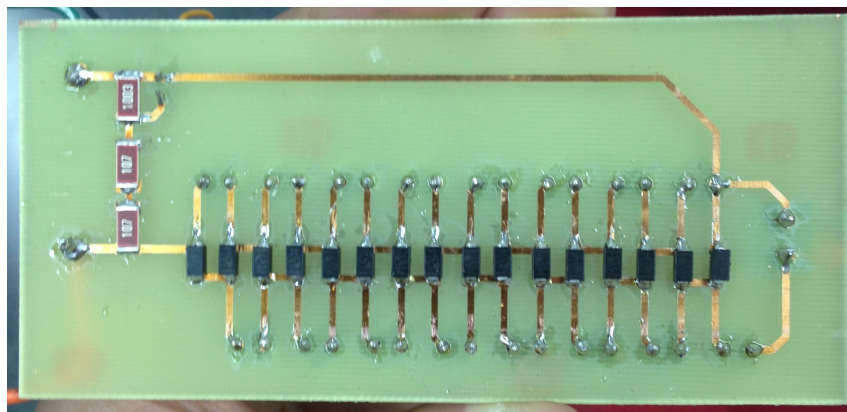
Resultado de la soldadura de componentes SMD en la etapa CW
